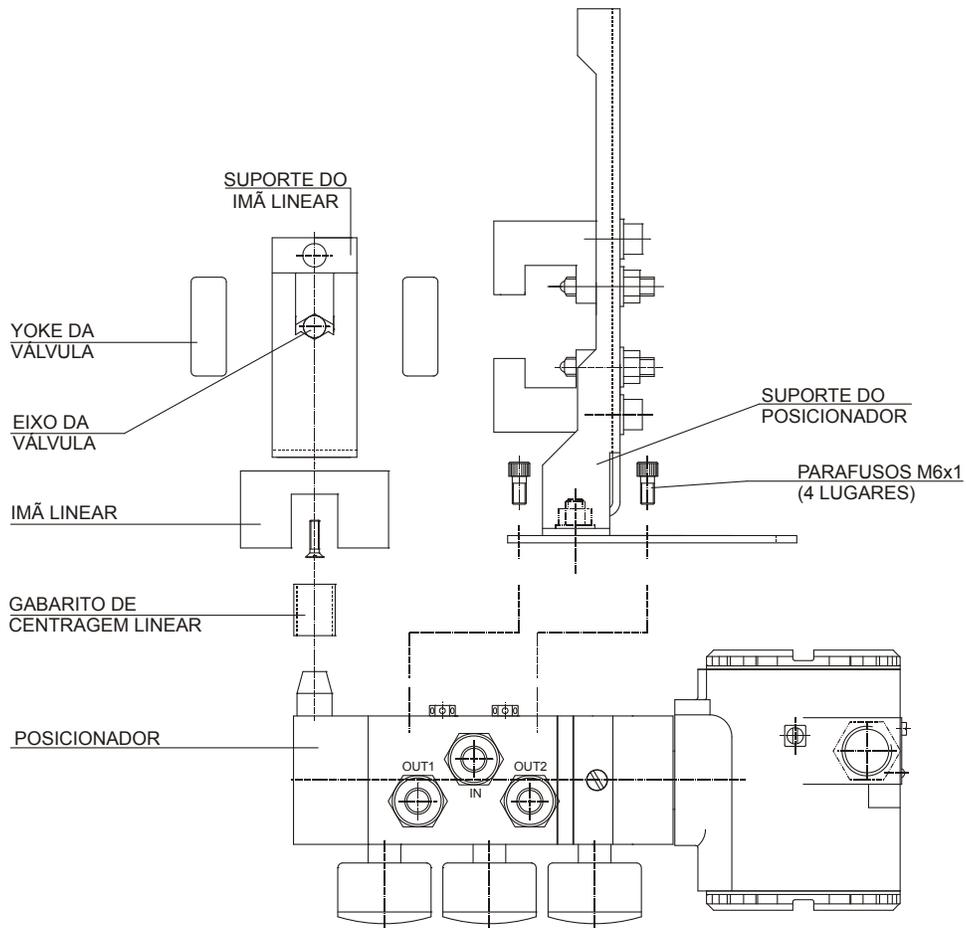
Esquema de Montagem do Posicionador em Atuador Linear
